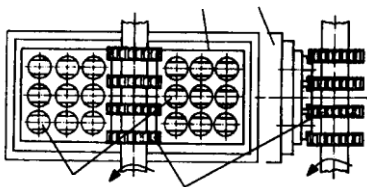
Фрезерування деталей, які встановлені поруч: 1 – деталі, що обробляються; 2 – набір фрез; 3 – стіл верстата; 4 – пристосування
